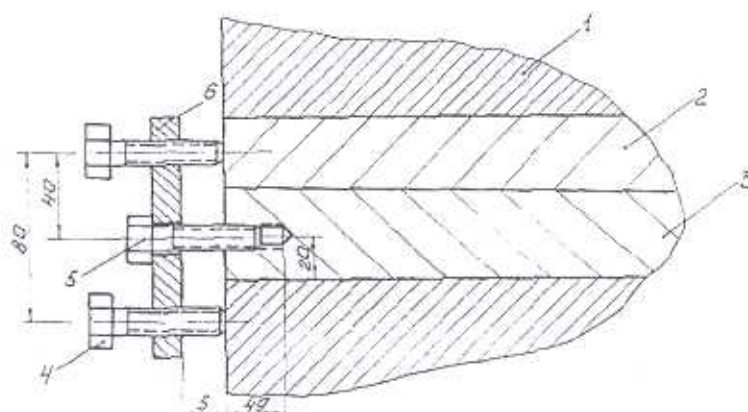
Приспособление для удаления шпонки полумуфты:
